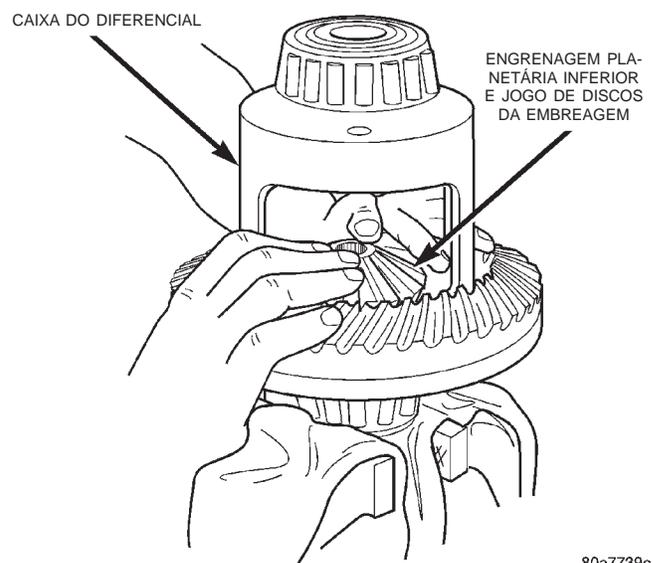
Discos da Embreagem e Instalação da Engrenagem Planetária Inferior
